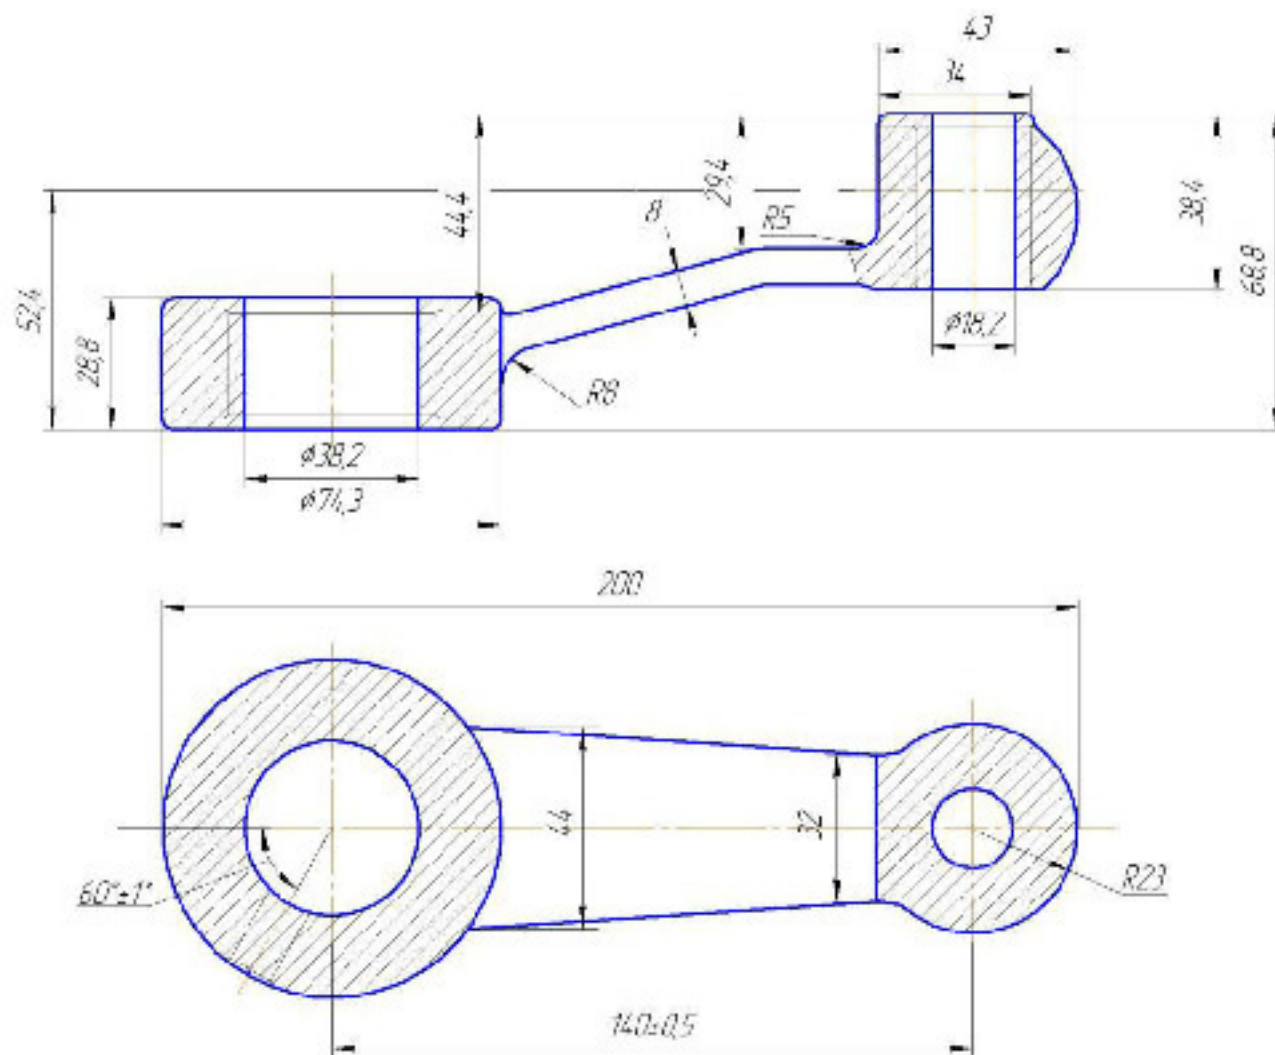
Ескіз заготовки при литті в оболонкові форми
